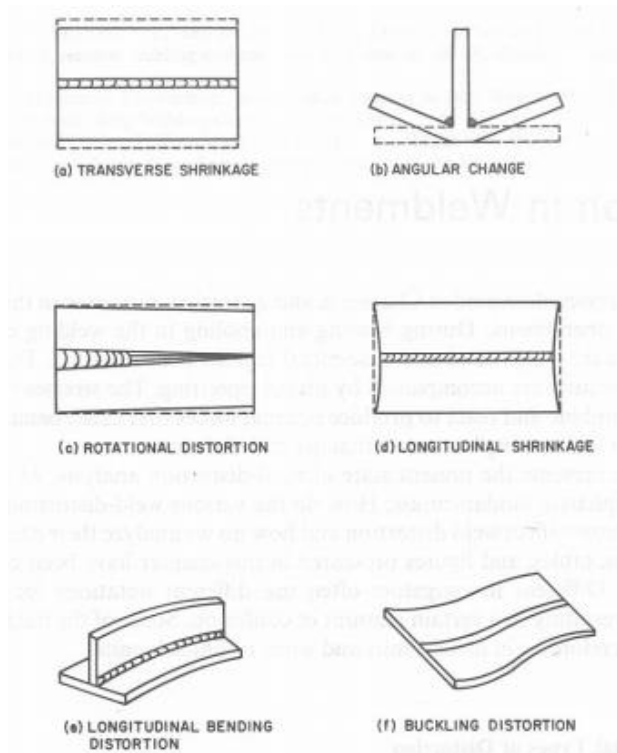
Vários tipos de distorções em soldadura, [11].
